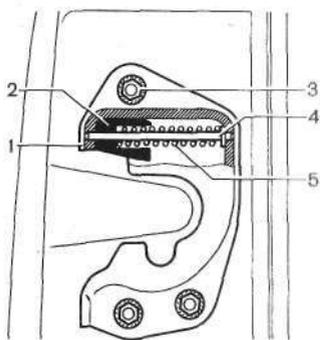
Фиксатор замка двери: 1 — корпус; 2 — сухарь; 3 — болт; 4 — ось; 5 — пружина
